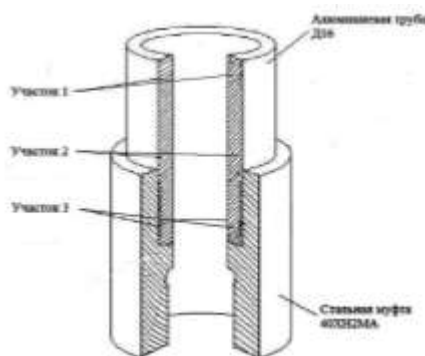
Схема вырезки образцов для исследований из алюминиевой трубы
